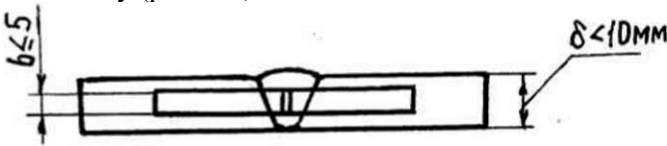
Схема вирізання зразка із зварного з'єднання товщиною менше 10 мм
